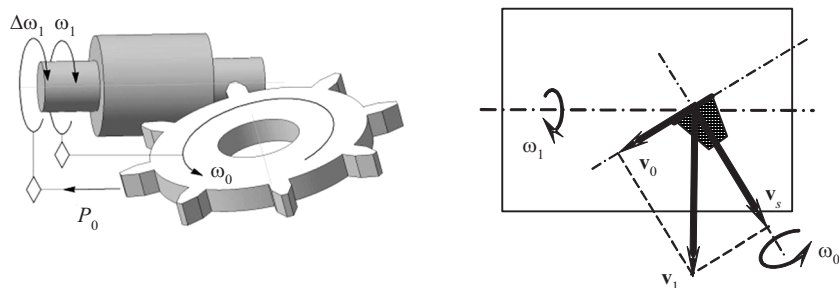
Схема нарезания червяка плоской резцовой головкой
